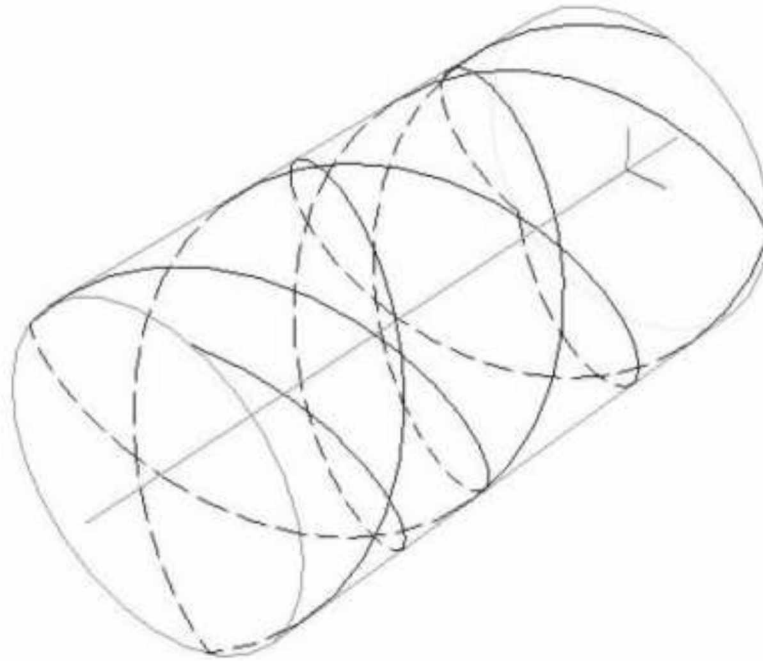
Траєкторія контакту з відновлюваною циліндричною поверхнею одного інструментального бруска
